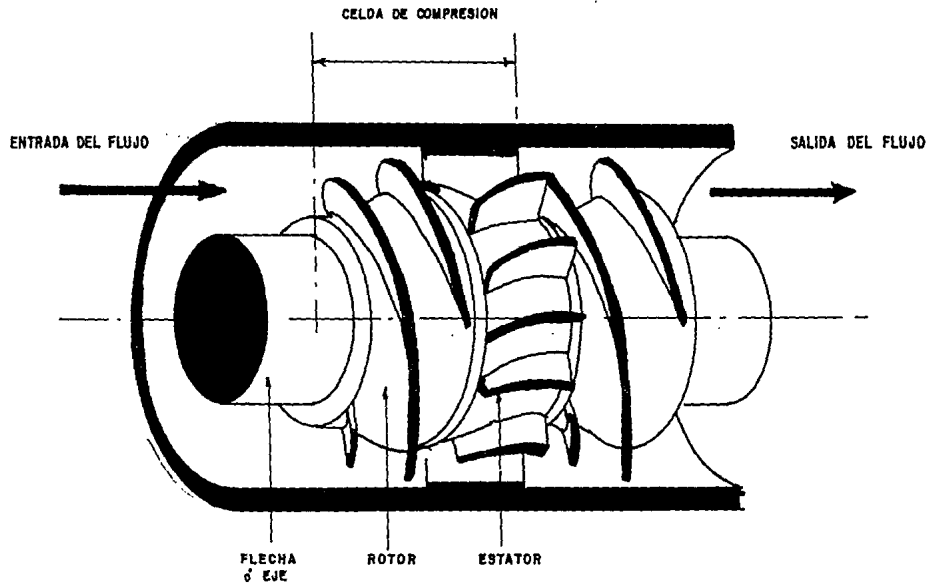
CELDAS DE COMPRESION HELICOAXIAL
